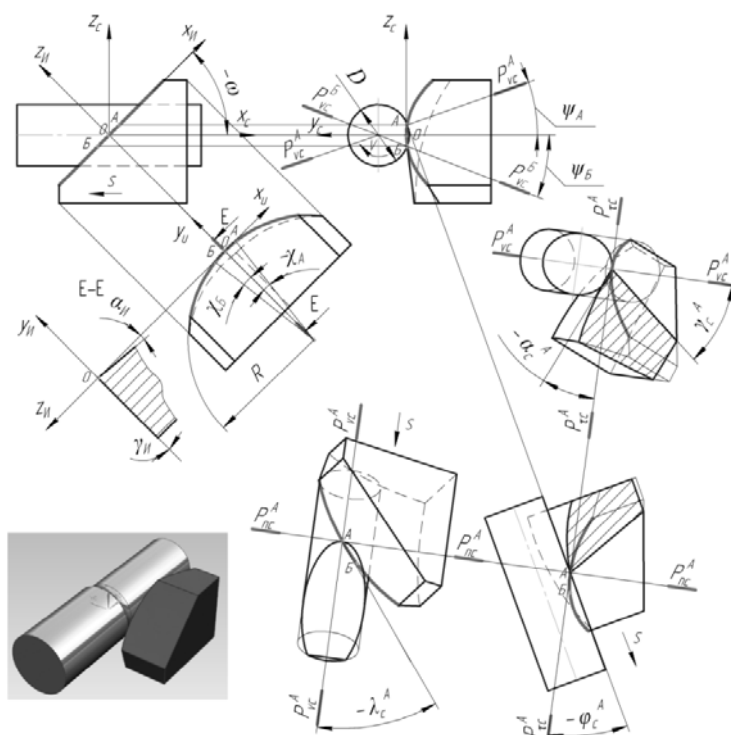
Схема косоугольного точения безвершинным резцом с радиальной режущей кромкой в статической системе координат, 3D модель процесса (I)х
